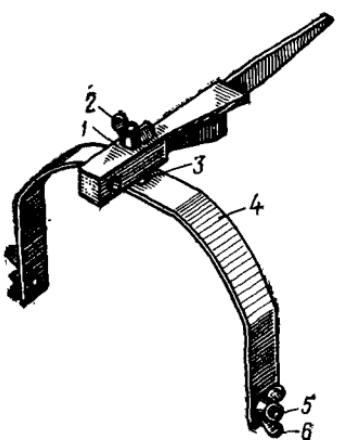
Приспособление для установки и крепления для мин, изготовленных до 1972 г.:
